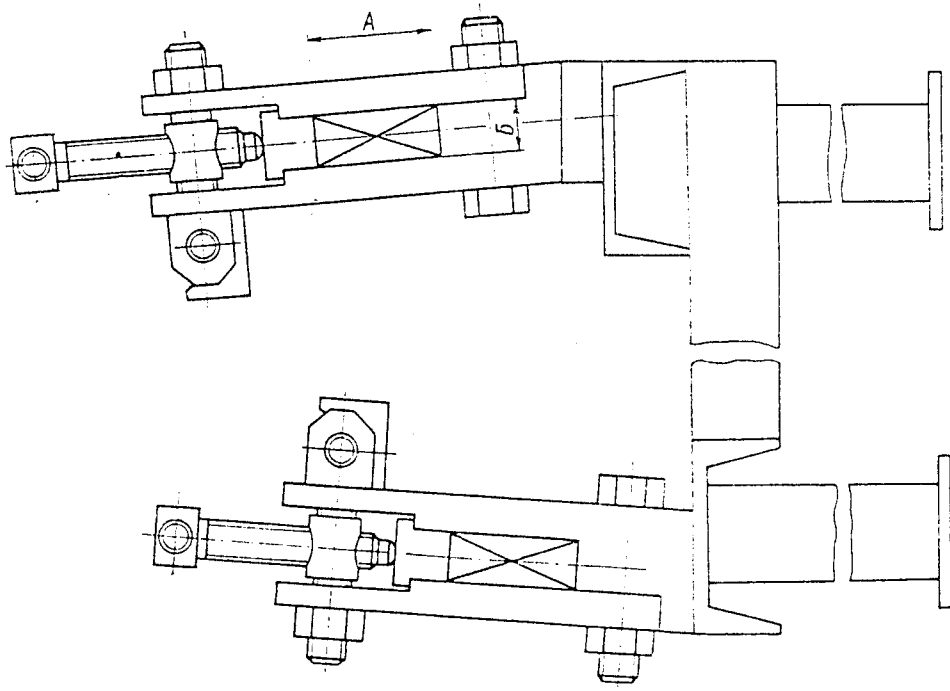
Пресс-форма для опрессовки пазовой части корпусной изоляции катушек
